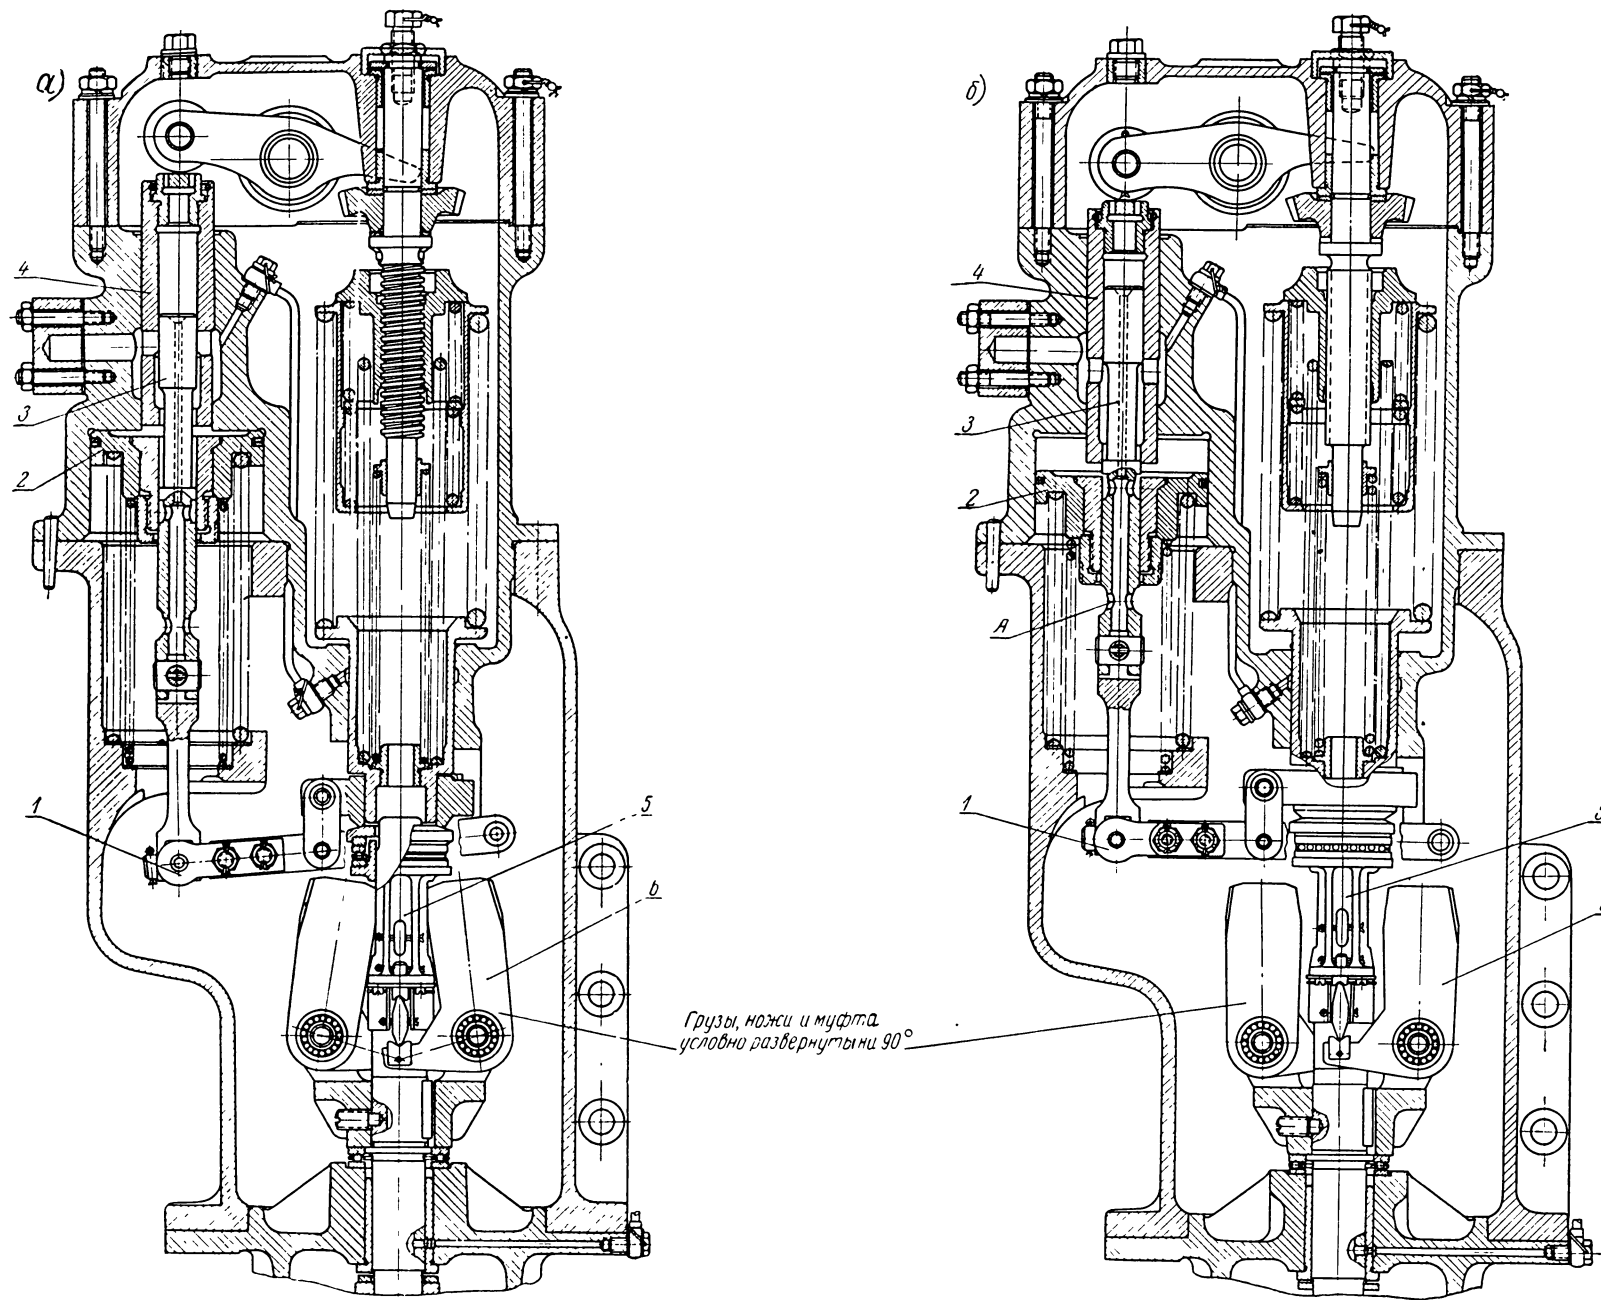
Регулятор: *a* — положение сервомотора при нормальной нагрузке; *б* — положение сервомотора при снятии нагрузки и увеличении числа оборотов.
